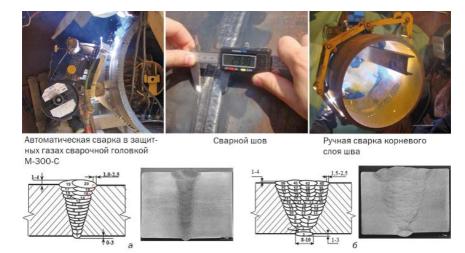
Квалификационные испытания технологии сварки кольцевых стыковых соединений и макрошлиф сварного соединения труб Ду1219 × 41,0 мм, выполненного автоматической (а) и ручной дуговой (б) сваркой при строительстве сухопутного участка морского газопровода «Nord Stream»
